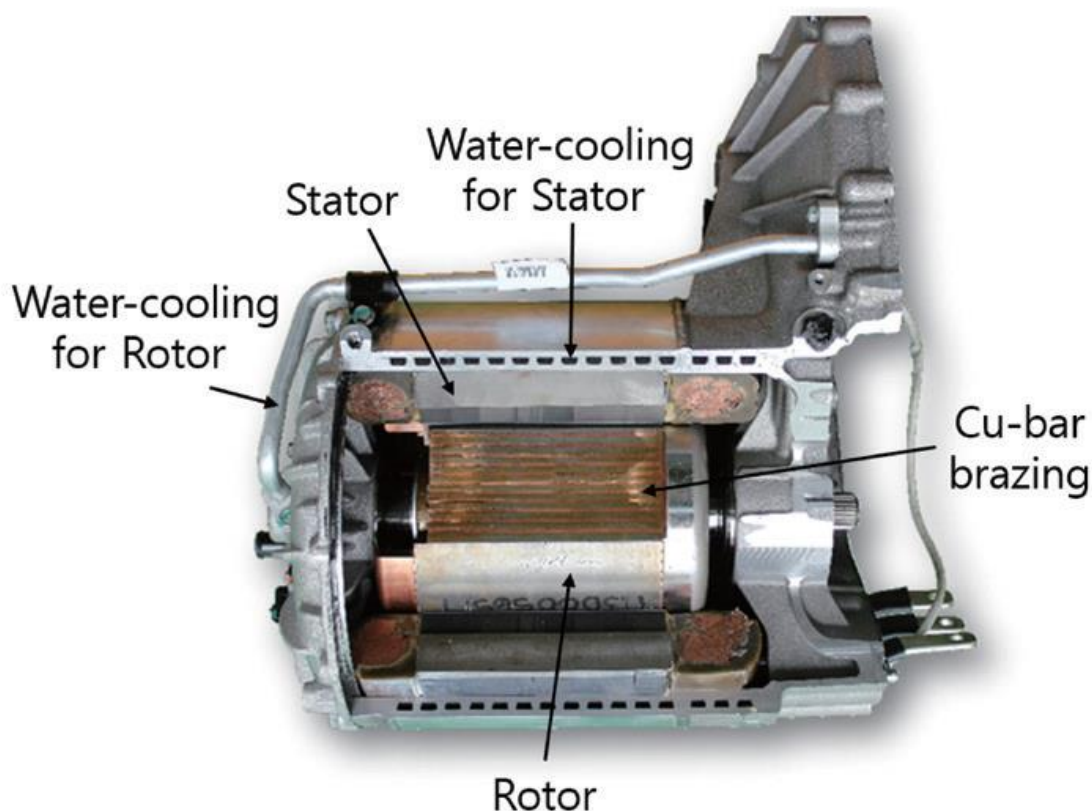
Приводной Двигатель Tesla Model S (Асинхронный Двигатель)
